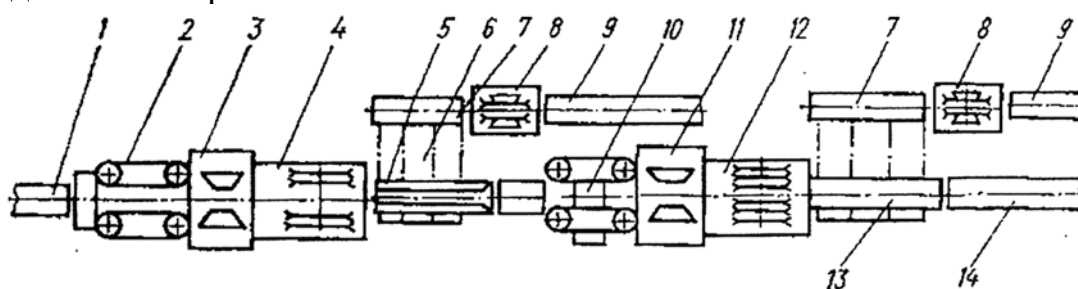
Схема потока на базе фрезернопильных и фрезерно-обрезных станков:
